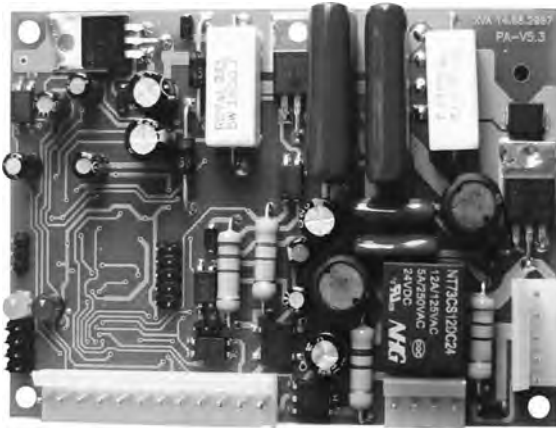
Плата контроллера PA-v5.3 для установок с мощными двигателями приводов подачи и высокими значениями коэффициента повторного включения
